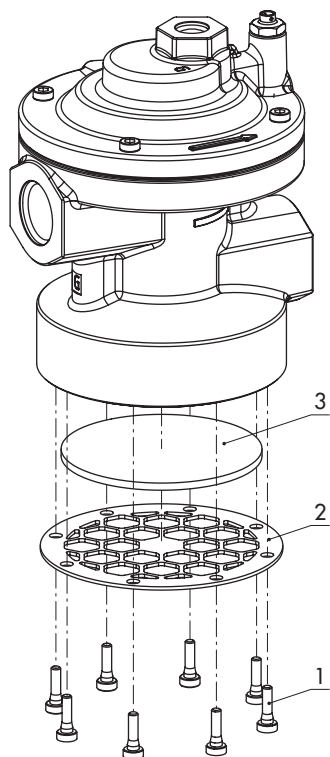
Тип 3755-1: шумопонижающий фильтрующий диск из порошкового полиэтилена
